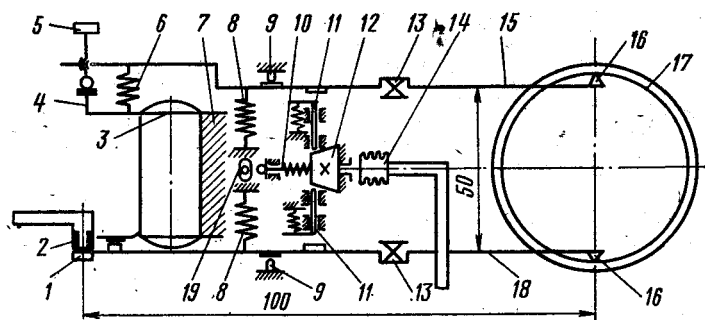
Схема устройства ОКБ-6К78 для автоматического контроля отверстий
